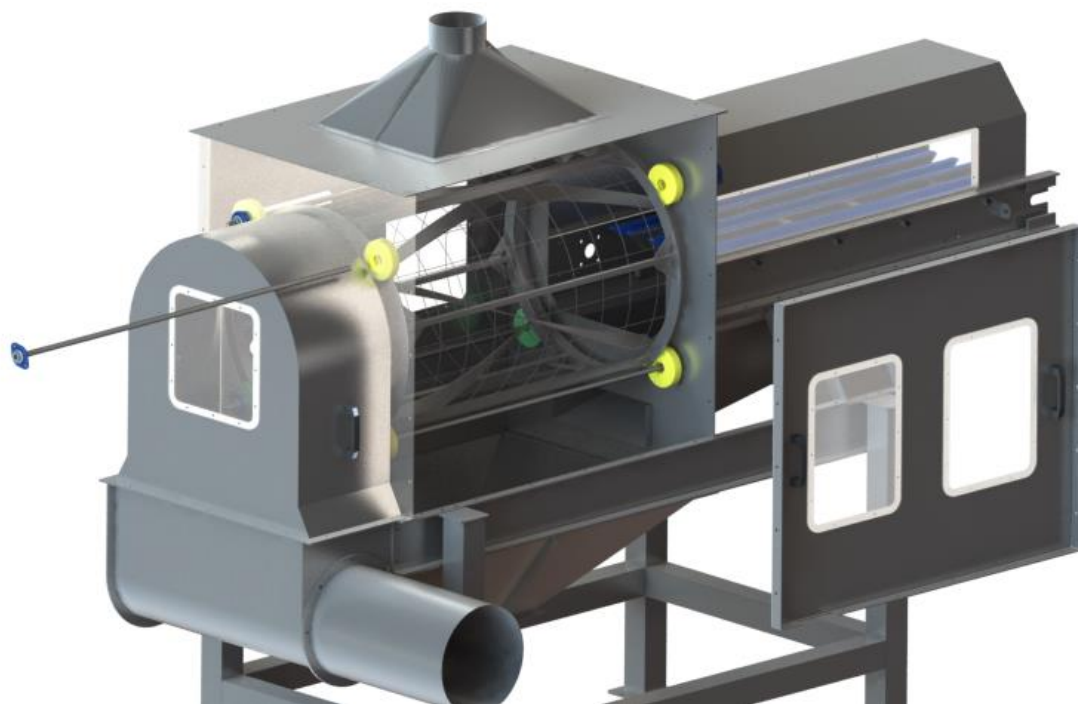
Desmontaje de chapa lateral, rodamientos
